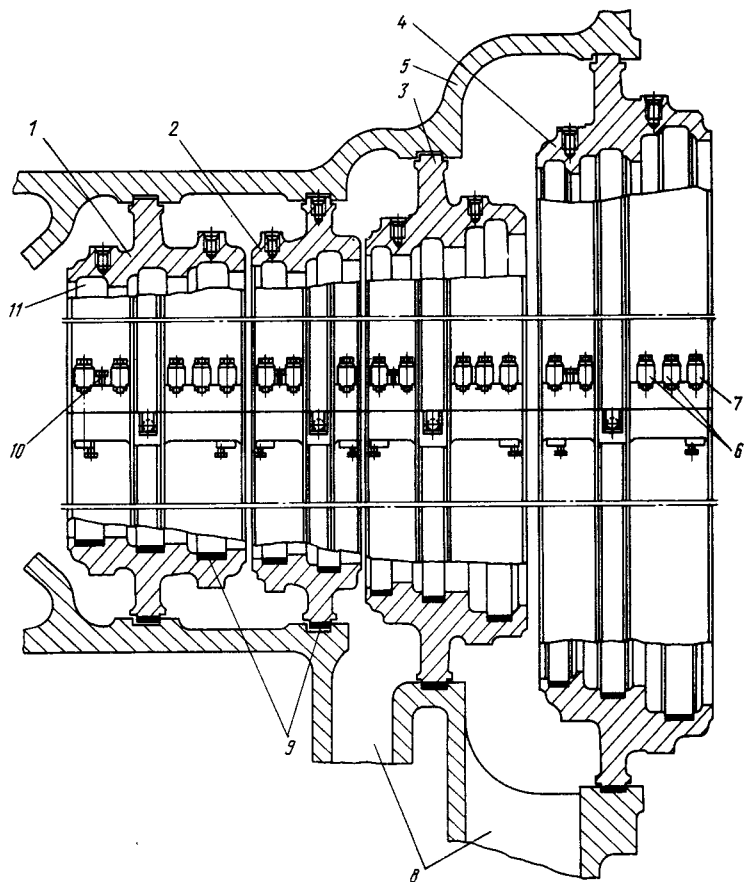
Установка обойм диафрагм в корпусе турбины:
